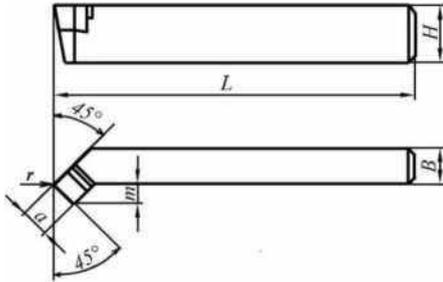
Резец токарный проходной, отогнутый с пластинками из твердого сплава (ГОСТ18877-73)
